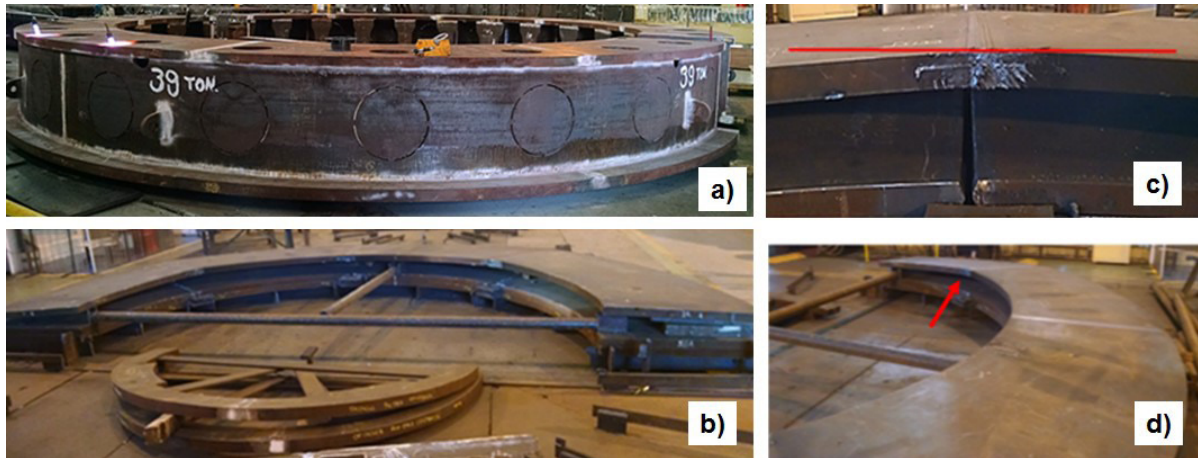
Estruturas soldadas e anéis segmentados em processo de fabricação.
